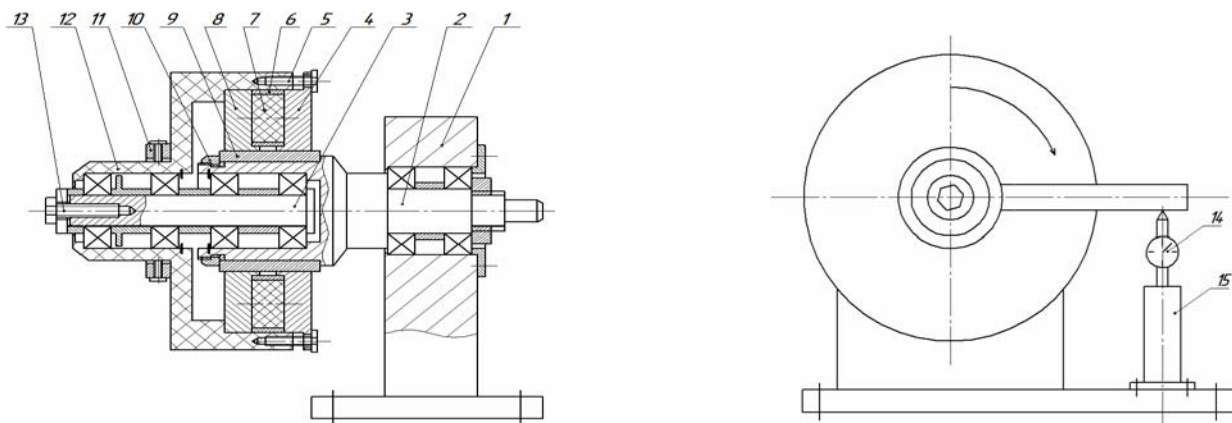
Схема экспериментальной установки: 1 – стойка; 2 – подвижный вал; 3 – неподвижный вал; 4 – съемный полюс; 5 – болт; 6 – диск; 7 – магнит; 8 – съемный полюс; 9 – сменная втулка; 10 – гайка; 11 – хомут; 12 – корпус; 13 – болт; 14 – индикатор; 15 – опора
